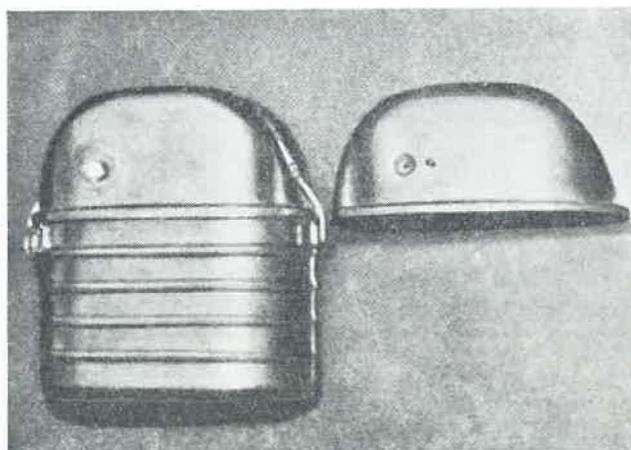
Petite ouverture ménagée dans le couvercle des masques Auer. Cette ouverture est normalement fermée par un point de soudure.
